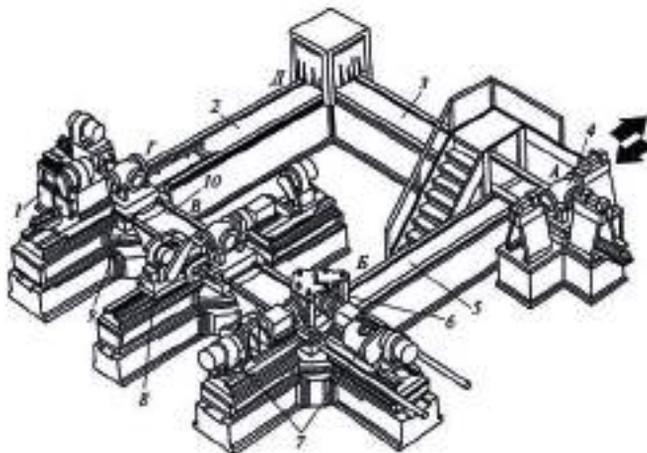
Однопредметная АЛ для обработки корпуса клапана с использованием приспособлений-спутников (ПС) и шаговых конвейеров:
